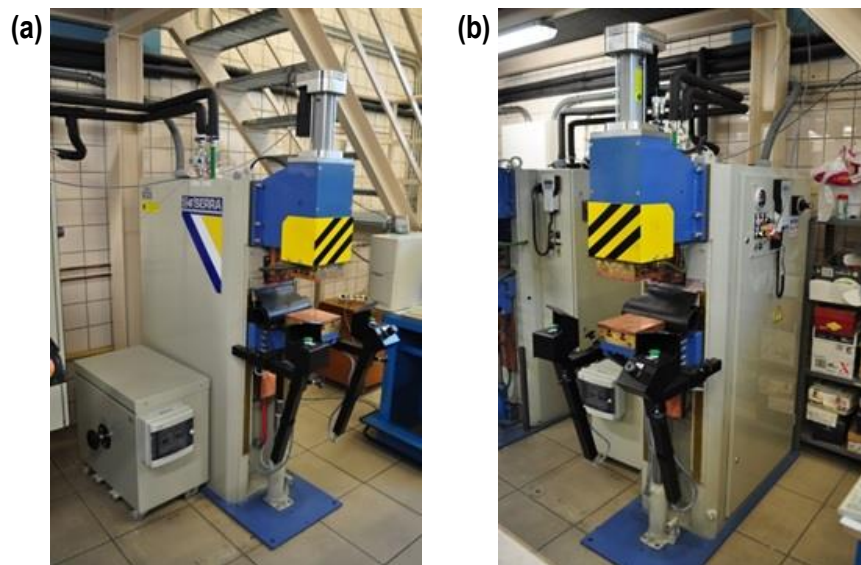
Máquina de soldadura por resistencia eléctrica (Beta-214 MF) adaptada para actuar como máquina de SRE-MF. Vistas: a) izquierda y b) derecha del equipo.
